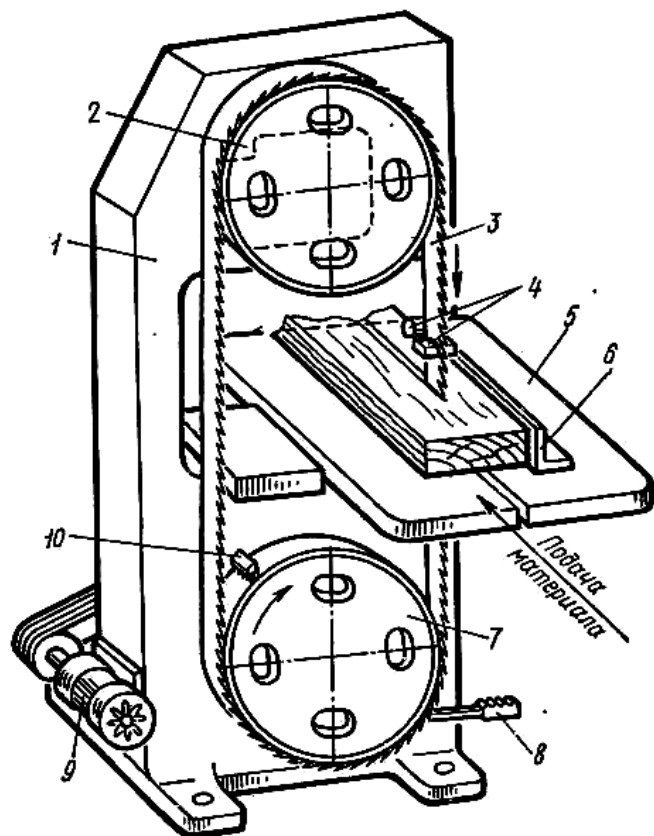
Станок ленточнопильный столярный с ручной подачей: 1 — станина, 2 — верхний неприводной шкив, 3 — пила, 4 — направляющее устройство, 5 — стол, 6 — направляющая линейка, 7 — приводной шкив, 8 — педаль тормоза, 9 — электродвигатель, 10 — щетка
